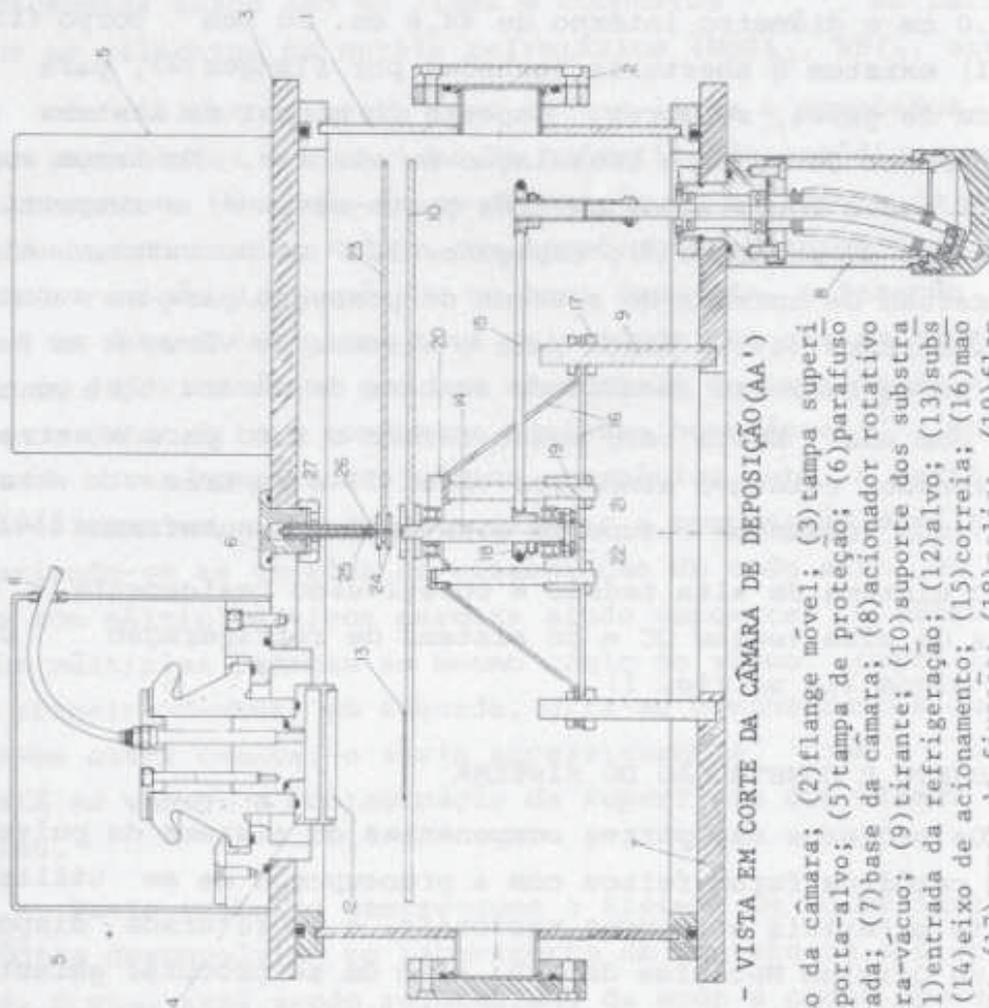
Fig. I - VISTA EM CORTE DA CÂMARA DE DEPOSIÇÃO (AA')
